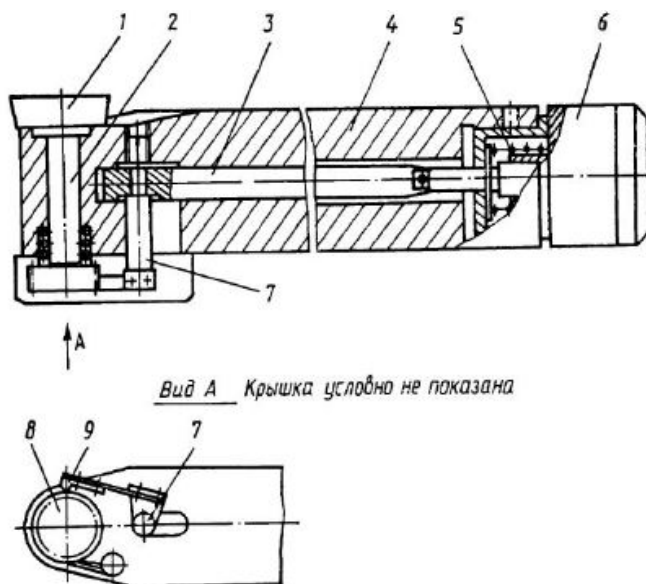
Чашечный резец с автоматическим периодическим поворотом режущей чашки
